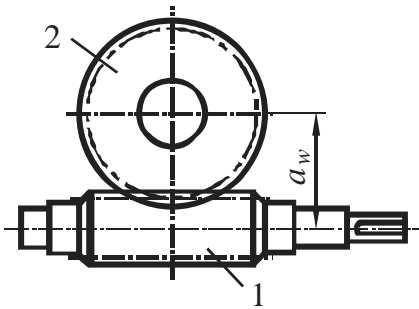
Схема червячного зацепления. 1 – червяк, 2 – червячное колесо
